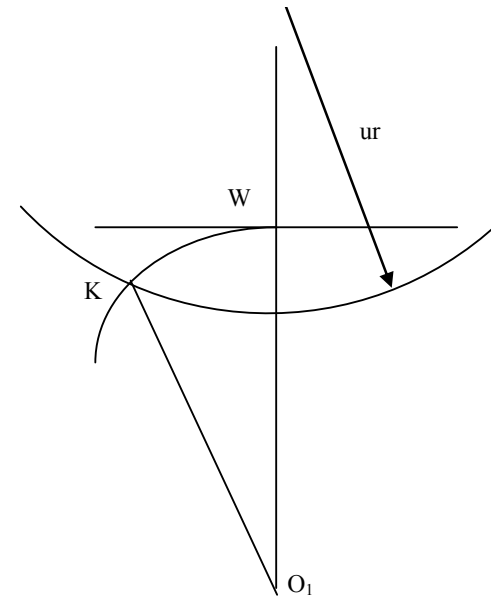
К определению коэффициента перекрытия в допальной зоне
